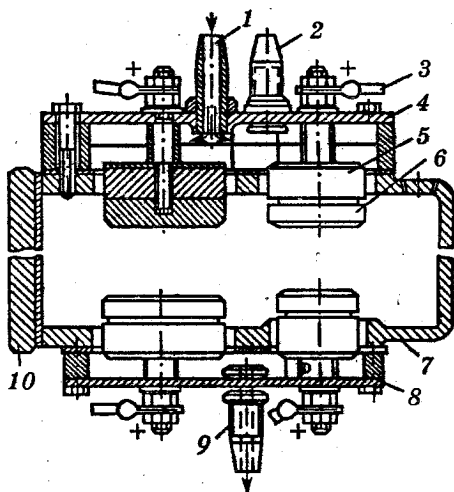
Схема электролитической ячейки для проточного осаждения металлов:
